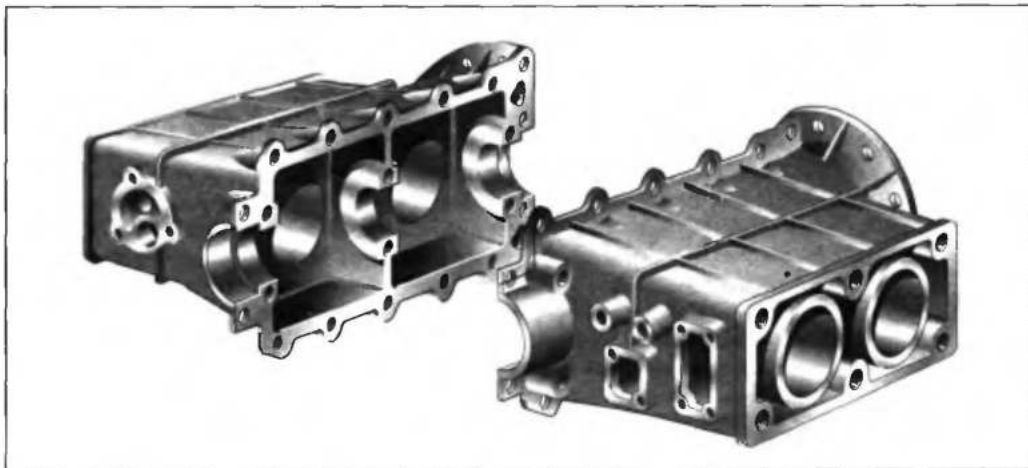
Разъемный блок-картер двигателя с оппозитным расположением цилиндров
